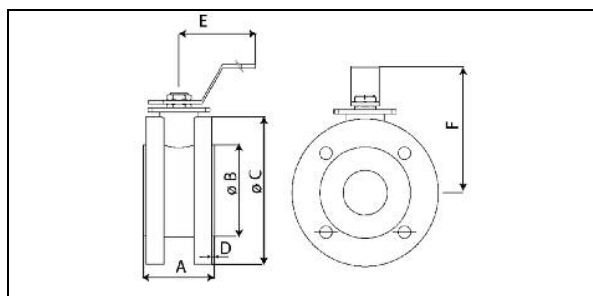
Габаритные размеры крана шарового типа X2900F.
